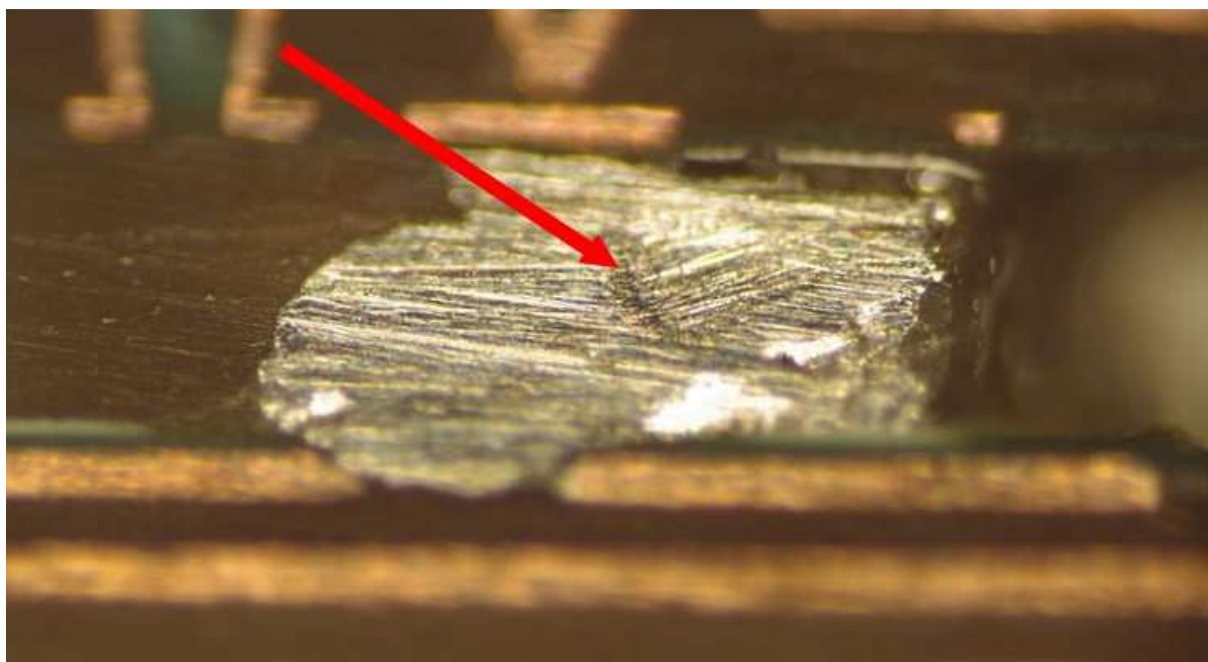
a obr. 63 ukazují defekty, jejichž původ je v neodpovídajícím tvaru dobře zapájenému spoji.
